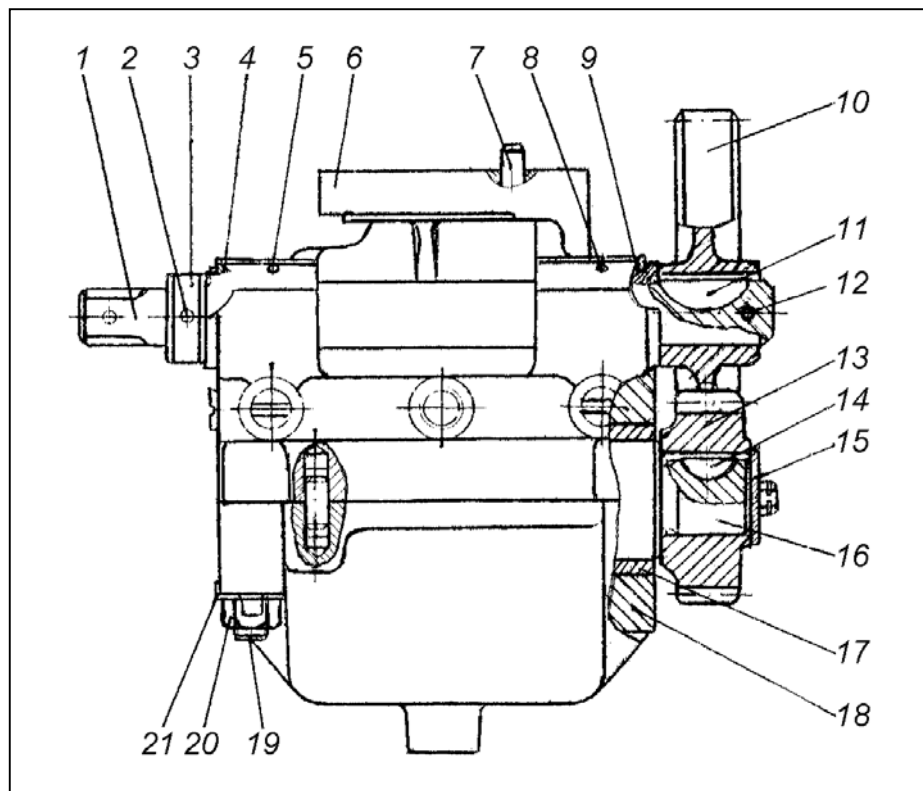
К сборке и установке уравнивающего механизма двигателей Д-160 и модиф.:
